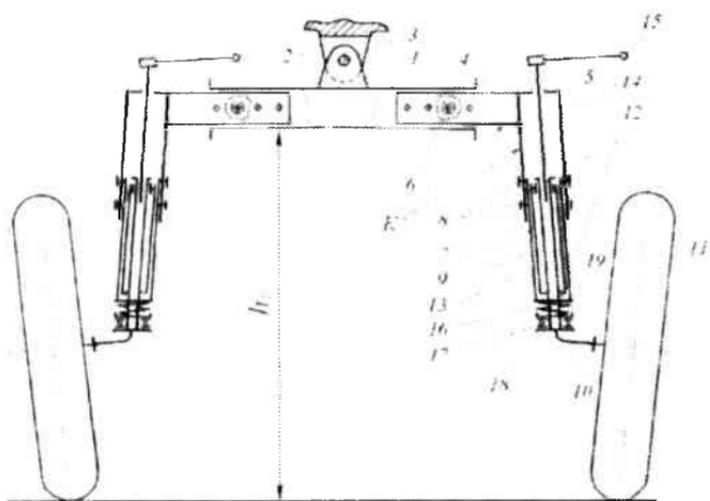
Схема переднего моста с выдвижным коленом, настроенным на высококлиренсный вариант: 1 – передний брус полурамы; 2 – ось; 3 – балка; 4 и 6 – полые трубы; 5 – рычаг механизма поворота; 7 – шлицевый вал; 8 – втулка; 9 – направляющее колесо; 10 – диск; 11 – цапфа; 12 – тарелка; 13 – упорный шарикоподшипник; 14 – пружина; 15 – обойма; 16 – шлицевая труба; 17 – подвижная труба; 19 – фиксатор; 18 – болт
